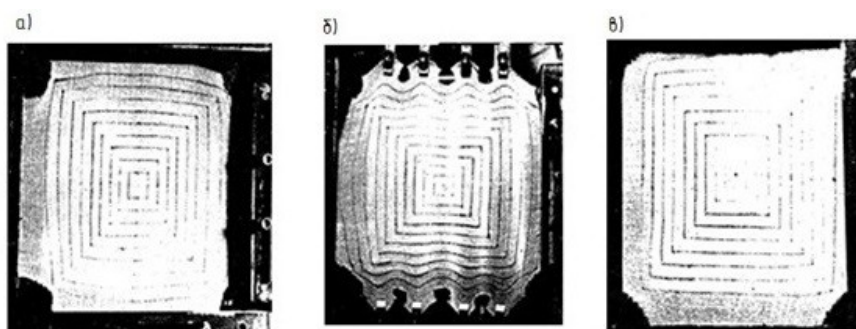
Фотографии деформированных образцов: а – крестообразная форма образца; б – форма образца с вырезанными полосками по сторонам; в – форма образца со срезанными углами
